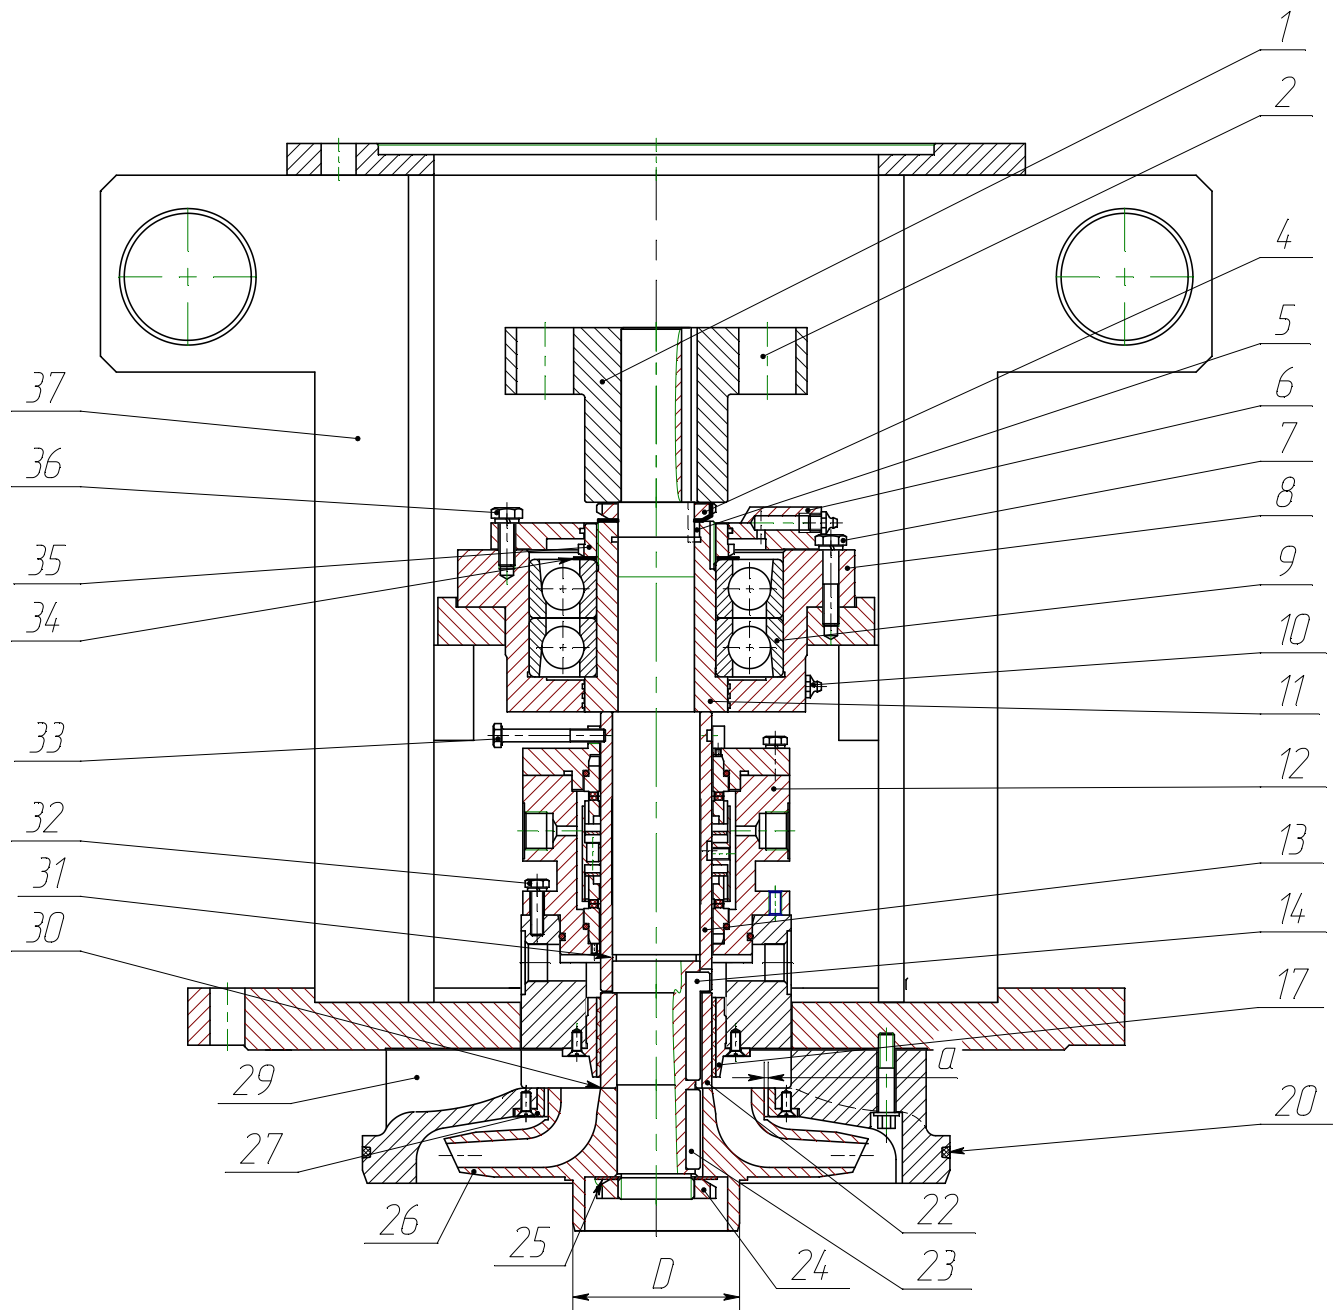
Быстроходная часть насосов (агрегатов)
